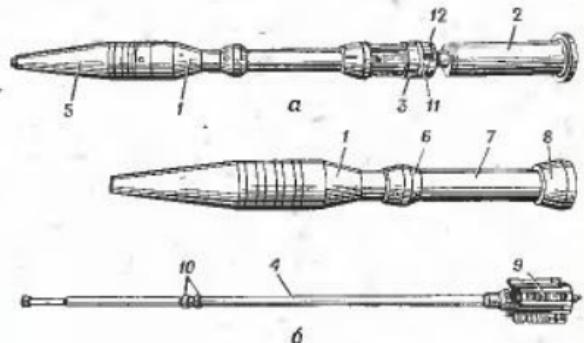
Приспособление для учебной стрельбы ПУС-9:
